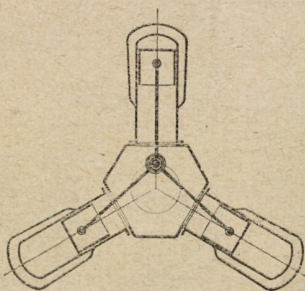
Motor „Barr a Stroud“ 1000 cm³.
